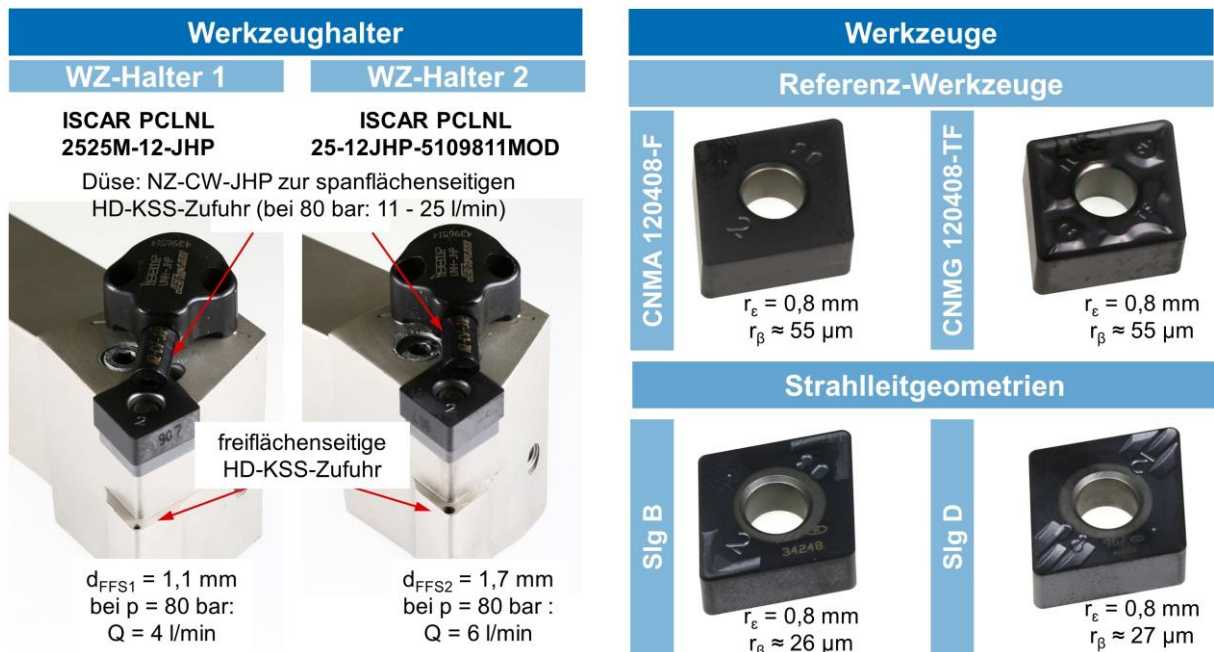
Eingesetzte sonderangefertigte Werkzeughalter und Werkzeuge
